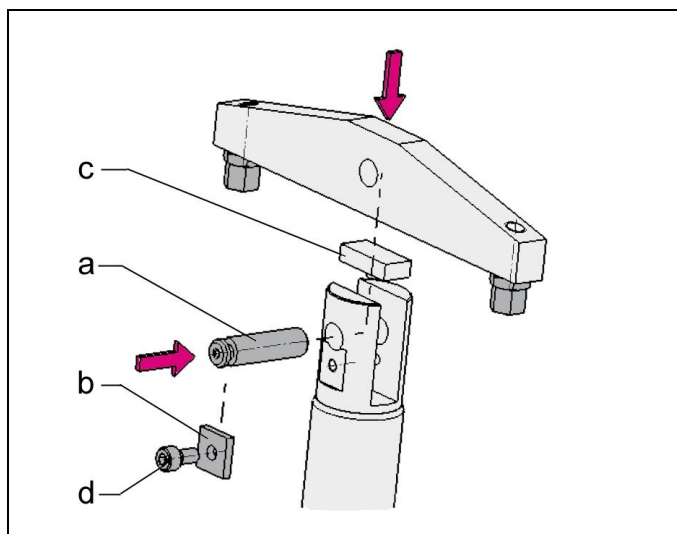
Montaje/desmontaje de la brida de sujeción con cabeza de horquilla
